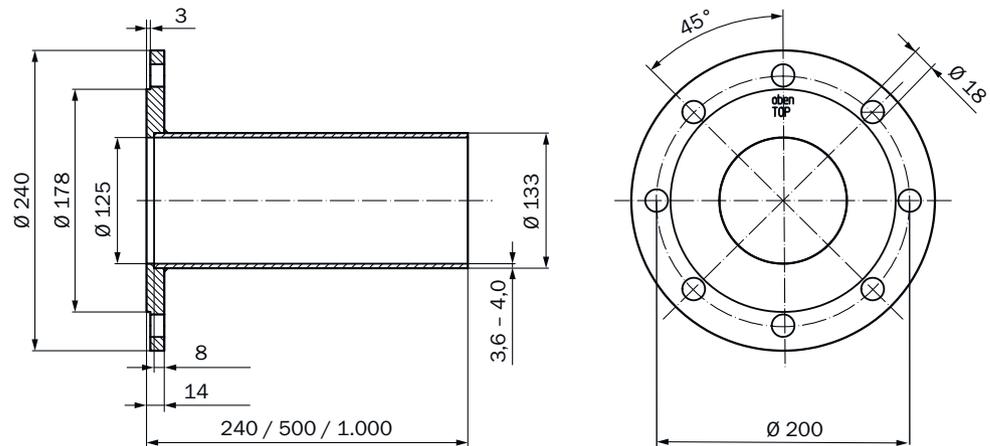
Flansch mit Rohr DN125 (Maße in mm)
